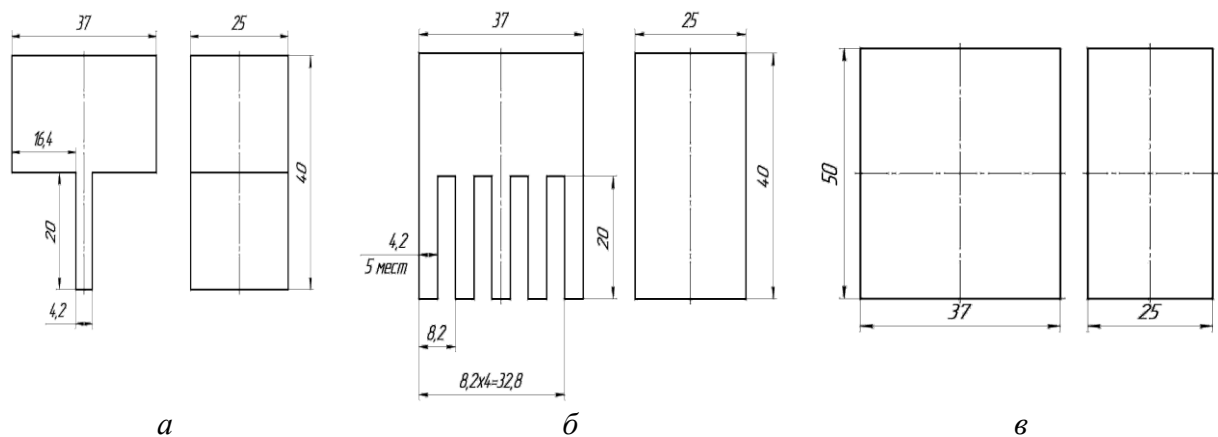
Форма и размеры моделей: a – пуансон с одним рабочим выступом; b – пуансон с пятью рабочими выступами; $в$ – заготовка [212]
